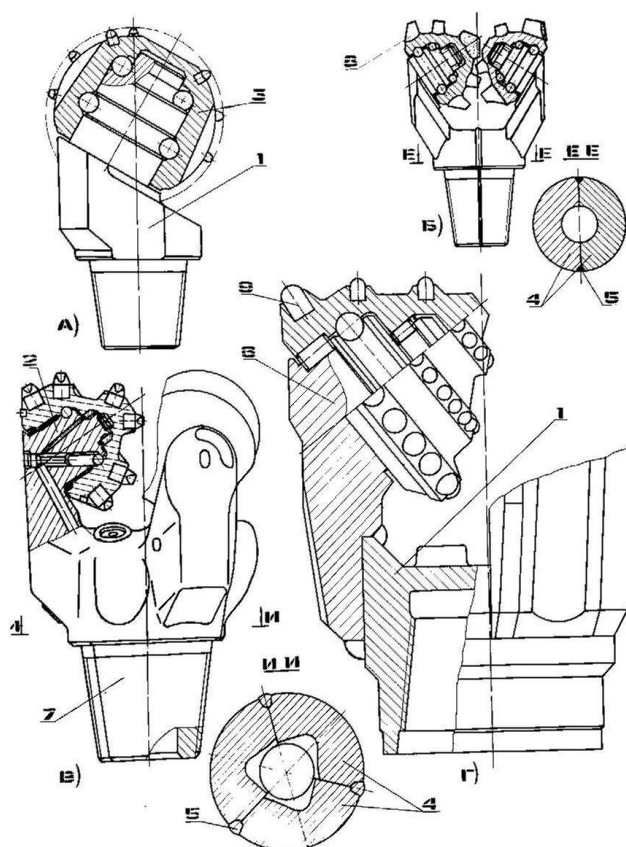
Конструктивное исполнение шарошечных долот: 1- корпус; 2 - цапфа; 3 - шарошка; 4 - секция; 5 - сварной шов; 6 - лапа; 7 - резьбовой ниппель; 8 - зуб фрезерованный; 9 – зуб вставной.
